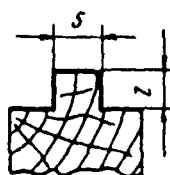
Фрезы для обработки пазов и гребней соединения К-3:
